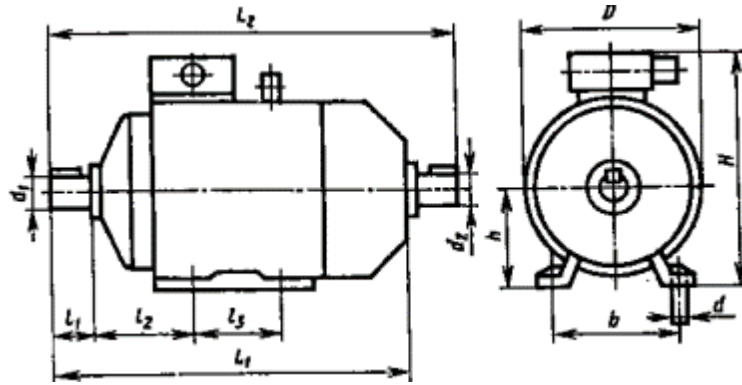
Габаритные и установочные размеры двигателя
